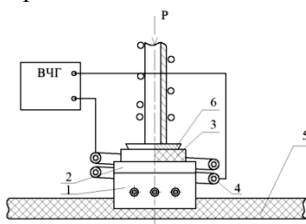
Схема ВЧ пайки корпусов микроблоков
